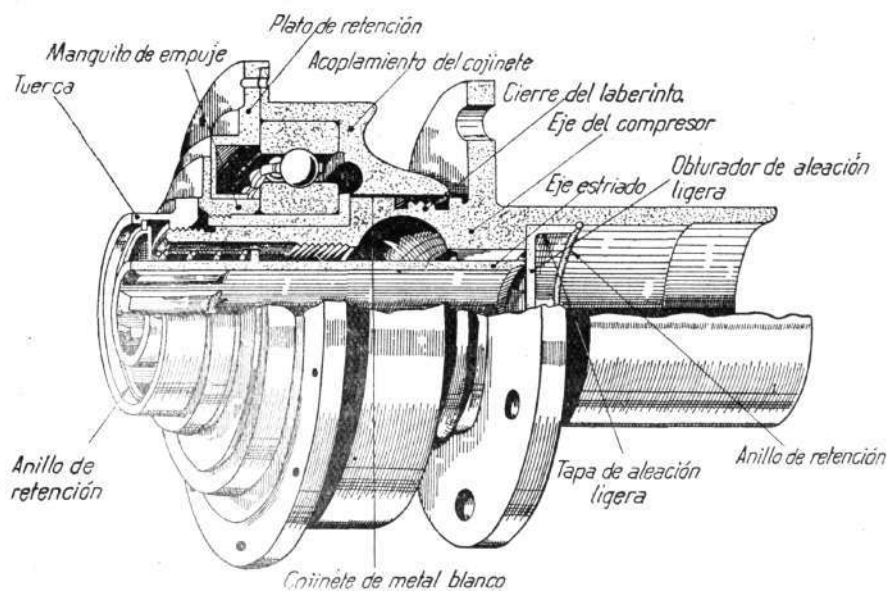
I. — Cojinete delantero del árbol motor del De Havilland Goblin II.
